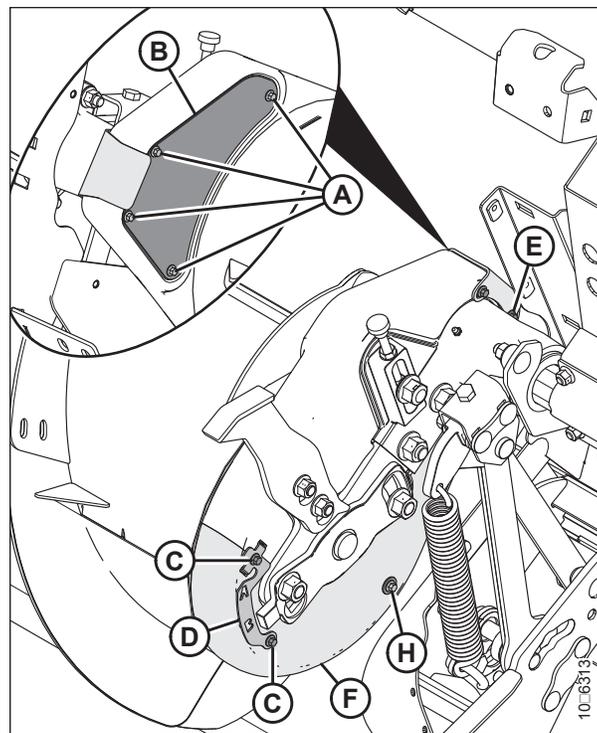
Einzugstrommelgetriebe – Rückansicht
